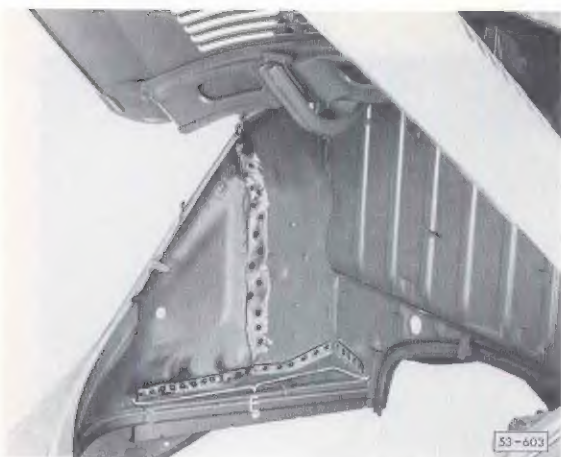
Seitenteil-Abschnittsteil, Motorabdeckblech und Abschlußblech hinten einschweißen.
